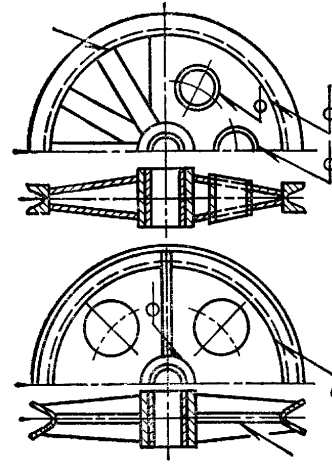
Сварные зубчатые колеса и шкивы
